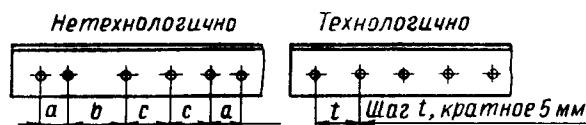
Схема расположения отверстий под заклепки на деталях профилей.
